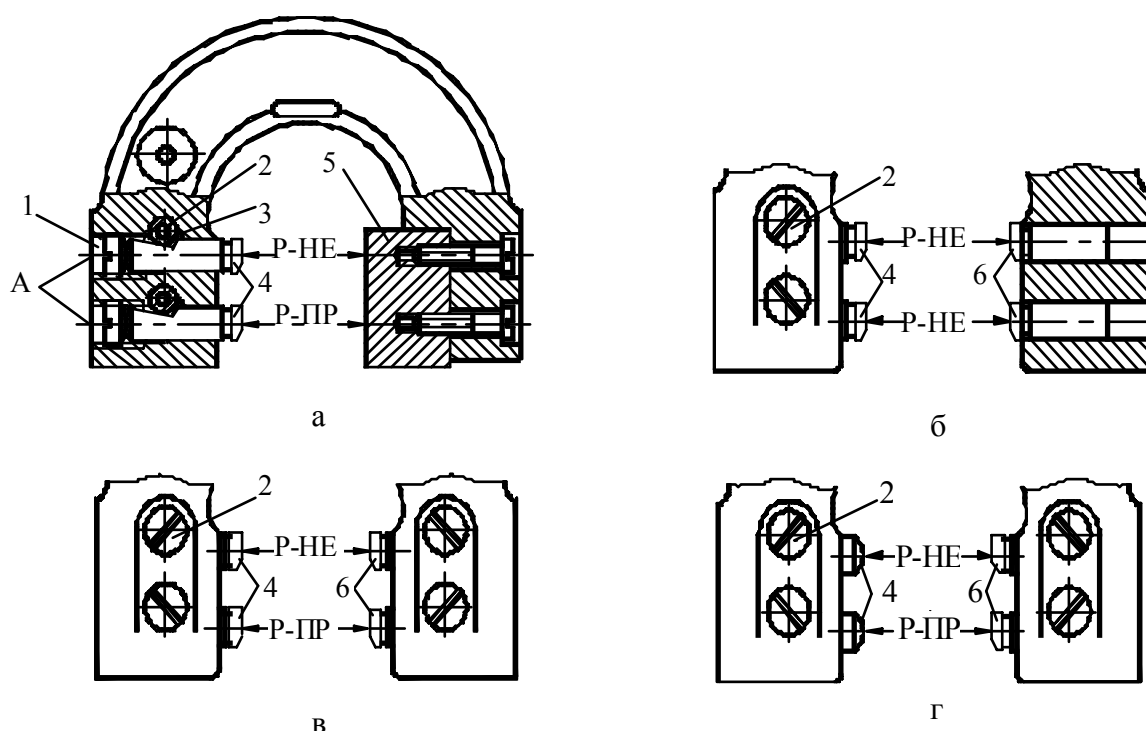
Конструкция регулируемых скоб: а – с неподвижной плоской губкой; б – с запрессованными (с правой стороны) цилиндрическими вставками; в – с двухсторонней регулировкой; г – с вставками со сферическими головками; 1 – установочный винт; 2 – затяжной винт; 3 – затяжная втулка; 4 – вставка; 5 – плоская вставка; 6 – цилиндрическая вставка
